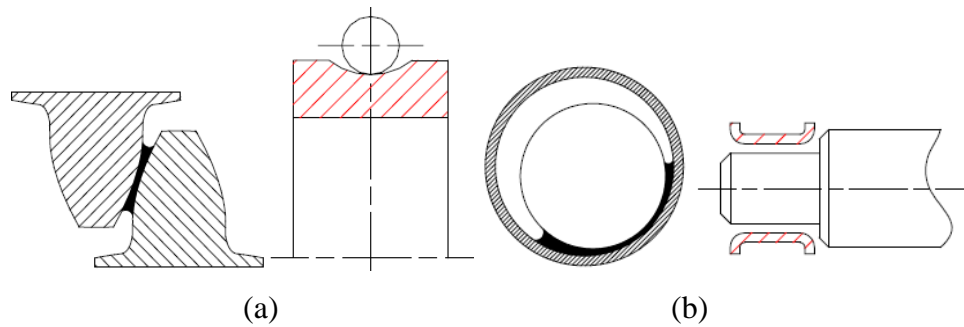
Contacts non-conformes (a - engrenage et roulement) et conformes (b - paliers)
